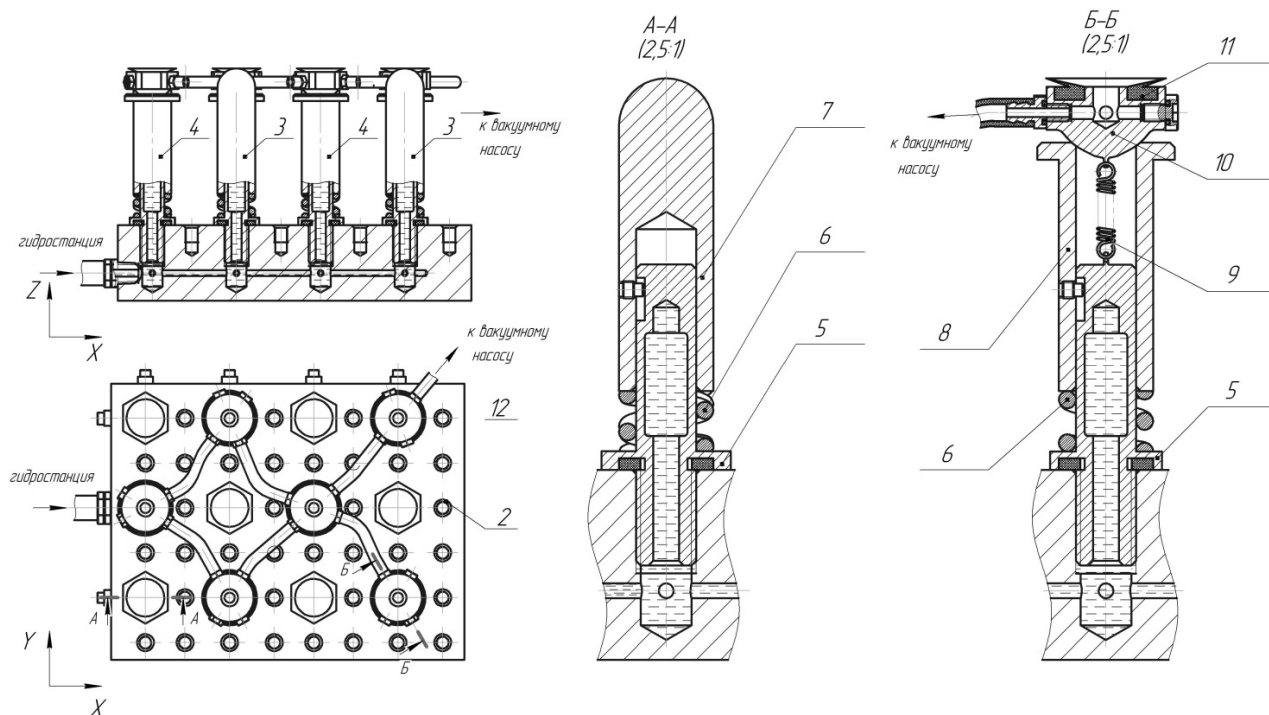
Приспособление для фиксации нежесткой заготовки сложного профиля
